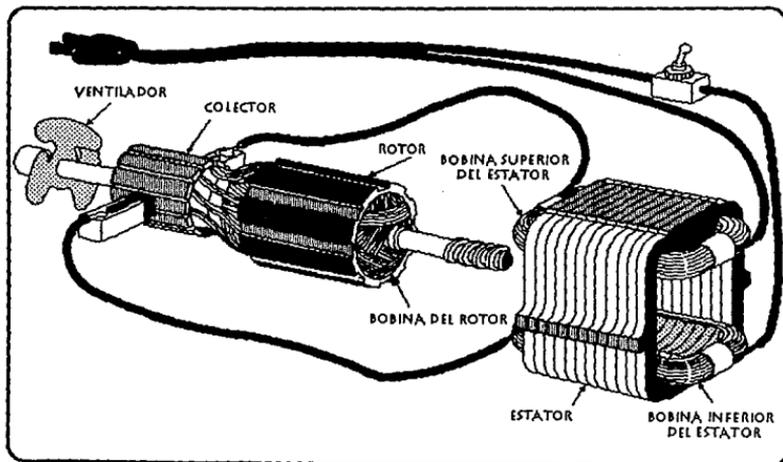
DESPIECE REPRESENTATIVO DE UN MOTOR UNIVERSAL.
